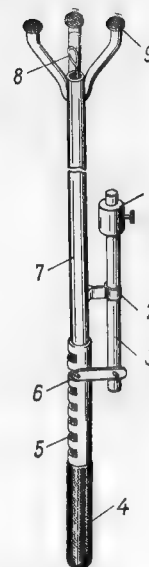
1 — груз; 2 — зажим; 3 — рычаг; 4 — ручка; 5 — труба с прорезями; 6 — вилка; 7 — штанга; 8 — трос; 9 — упор
